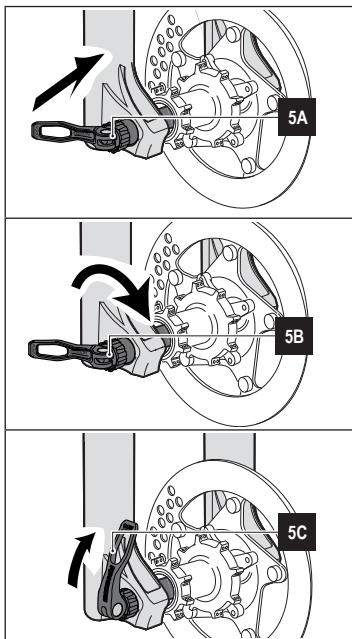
QR15 oder QR20 "quick release" Steckaxle - Laufradbefestigung
